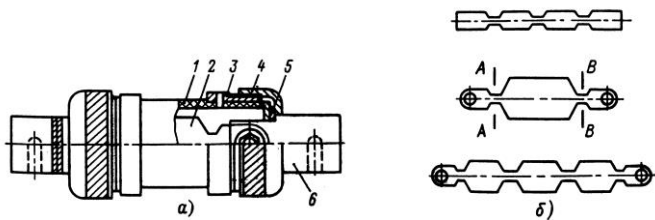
Запобіжник типу ПР-2: а - патрон на номінальні струми 100...1000 А; б - форми плавких уставок
